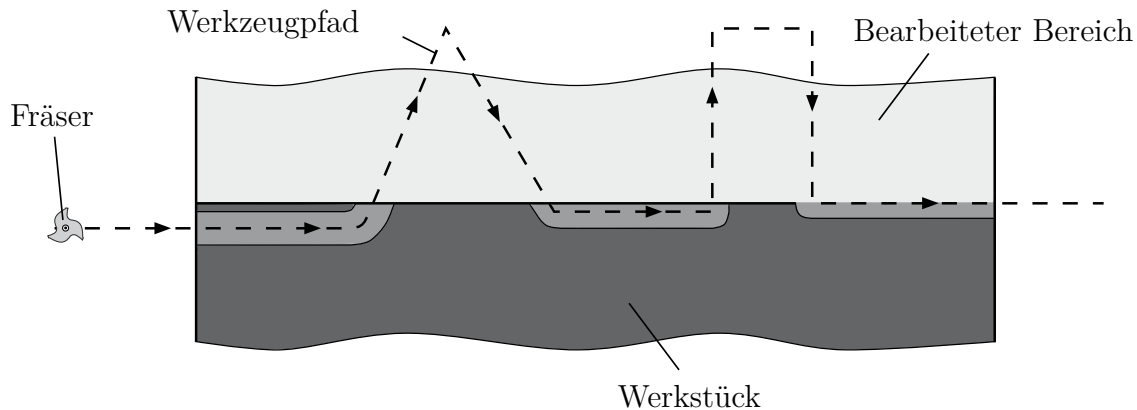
Draufsicht auf das bearbeitete Werkstück mit eingezeichneten Werkzeugpfad.
